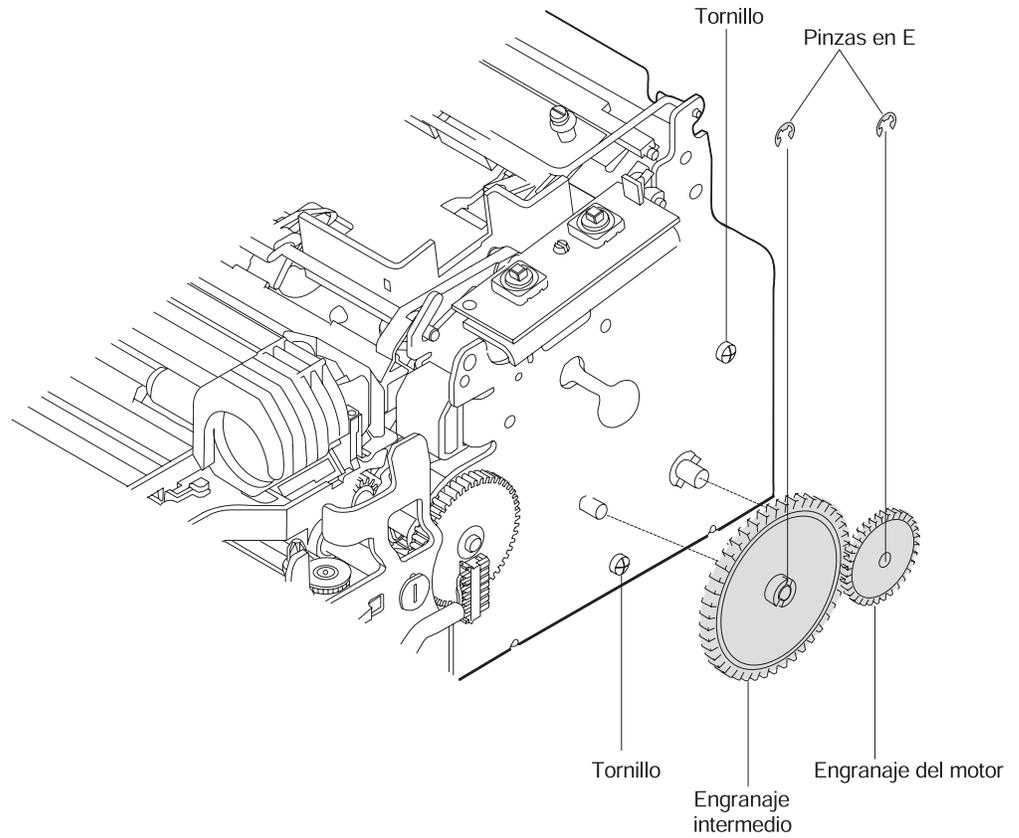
Extracción del engranaje del motor y del engranaje intermedio
